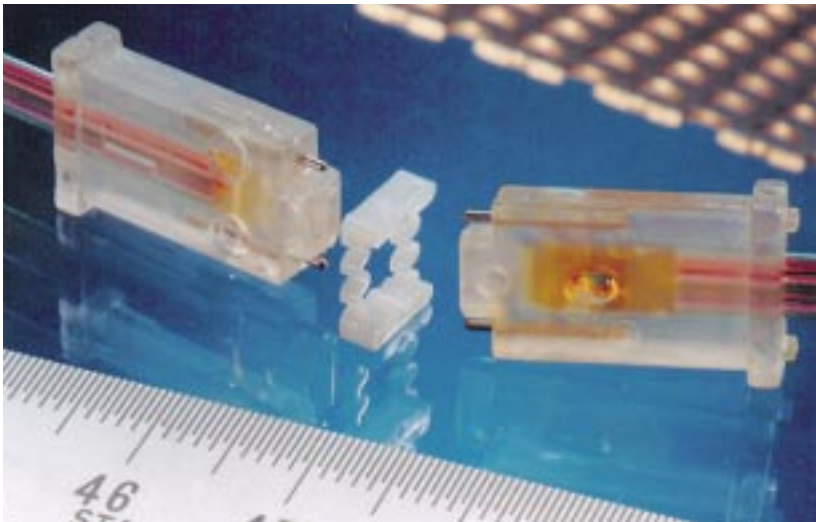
Zwei fertig montierte Faserstecker mit verbindendem Koppelement.
